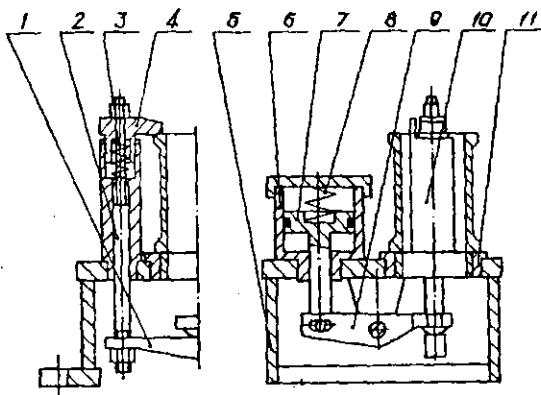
24. Приспособление для растачивания гильзы цилиндра:
